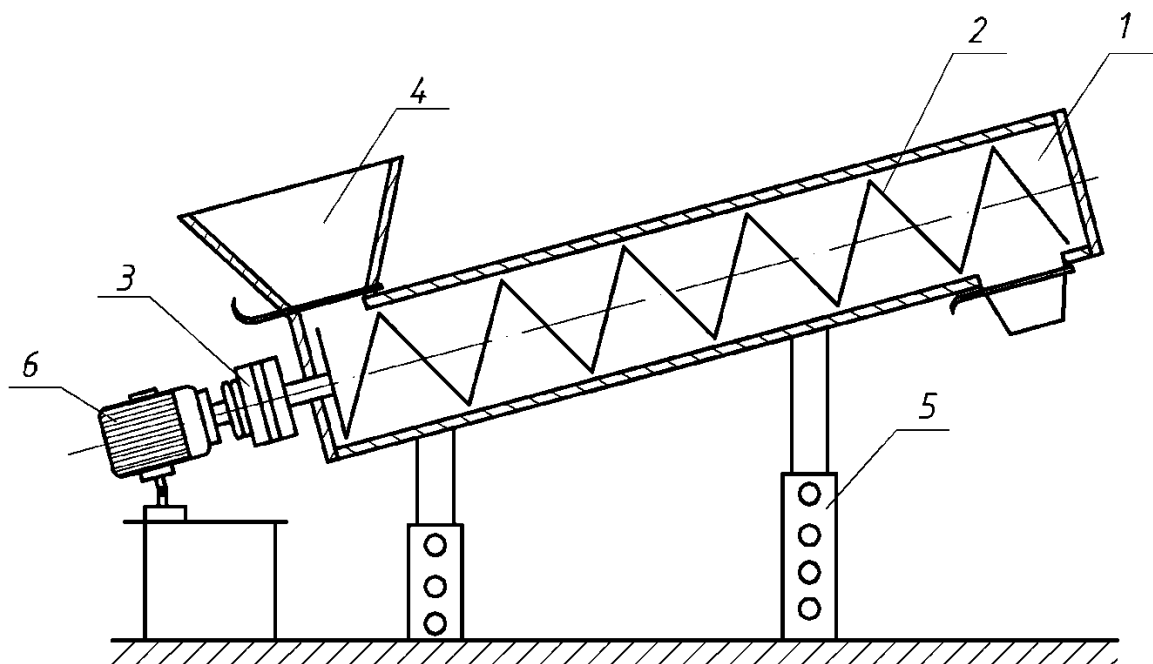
Модель транспортно-технологічної системи з гвинтовим робочим органом: 1 – жолоб; 2 – гвинтовий робочий орган; 3 – механізм передачі крутного моменту; 4 – бункер; 5 – опорно-регулювальний механізм; 6 – двигун-редуктор
